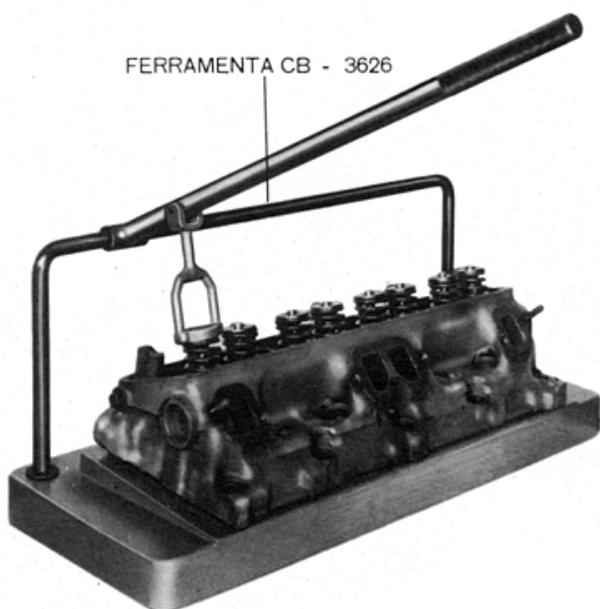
Suporte do cabeçote e compressor das molas das válvulas
